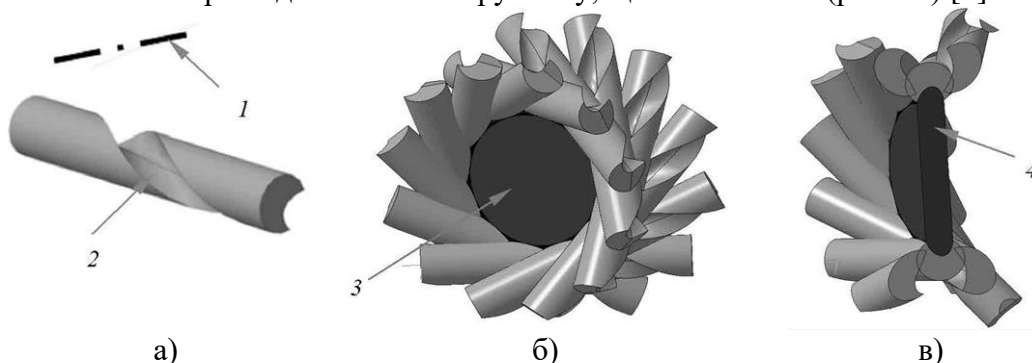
Етапи визначення ВІП дискового інструменту для оброблення гвинтової канавки свердла: а) модель свердла з віссю інструмента; б) побудова послідовних положень деталі – масив по колу; в) визначення осьового перерізу ВІП дискового інструменту, 1 – вісь ВІП, 2 – гвинтова поверхня деталі, 3 – поверхня ВІП і сімейство поверхонь деталі, 4 – осьовий переріз ВІП.
